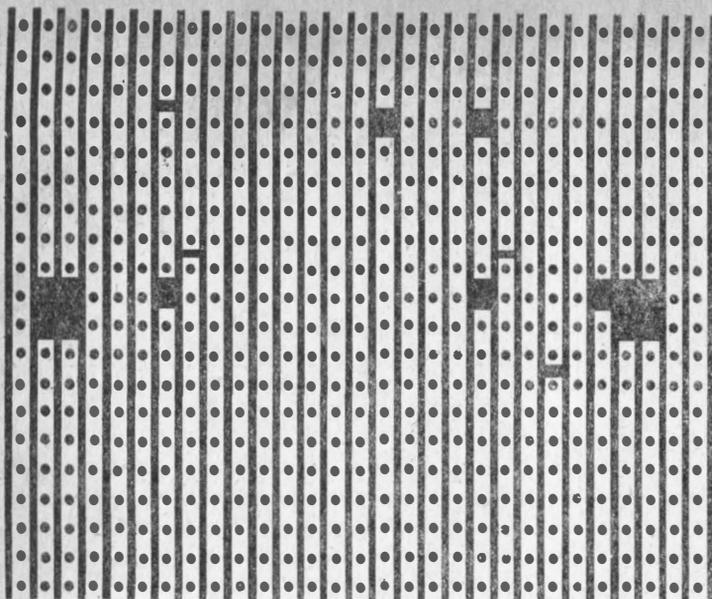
Plaqueta de circuito impresso universal, com as interrupções a serem feitas nos filetes de cobre, para a montagem do filtro.
